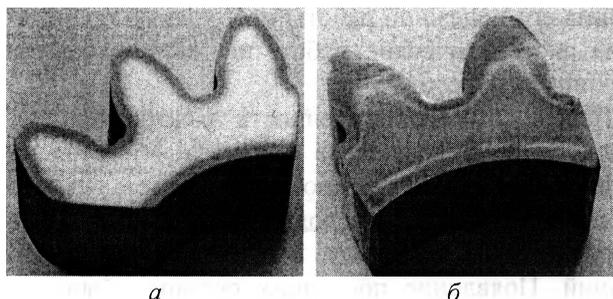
Фотография макрошлифа фрагмента детали сателлит: а — из стали 20ХНЗА, прошедшей операцию цементации, б — из стали 60ПП с объёмно-поверхностной закалкой
